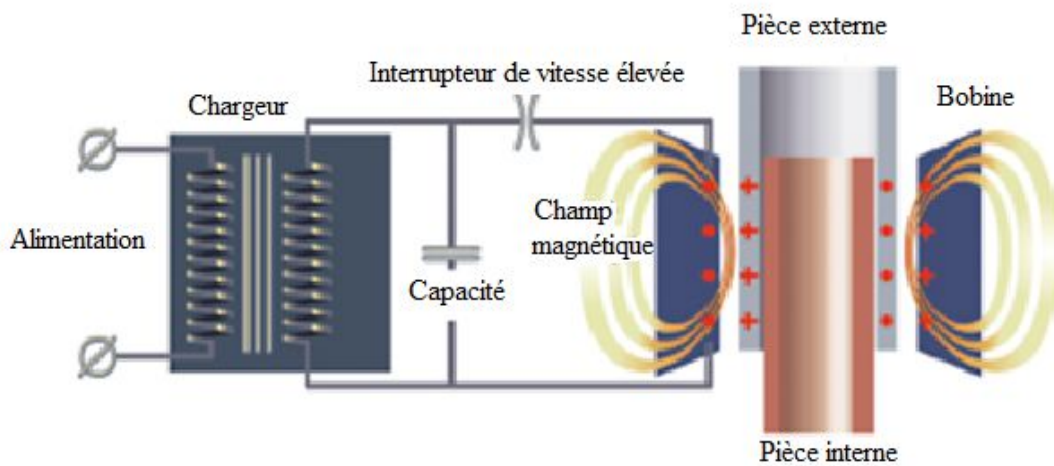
Soudage par impulsion magnétique [14].
